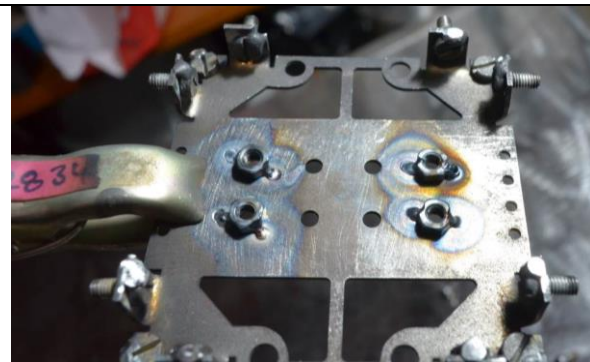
Detalle tapa de "jaula", se aprecia sistema de tornillería para ensamble y desensamble.
